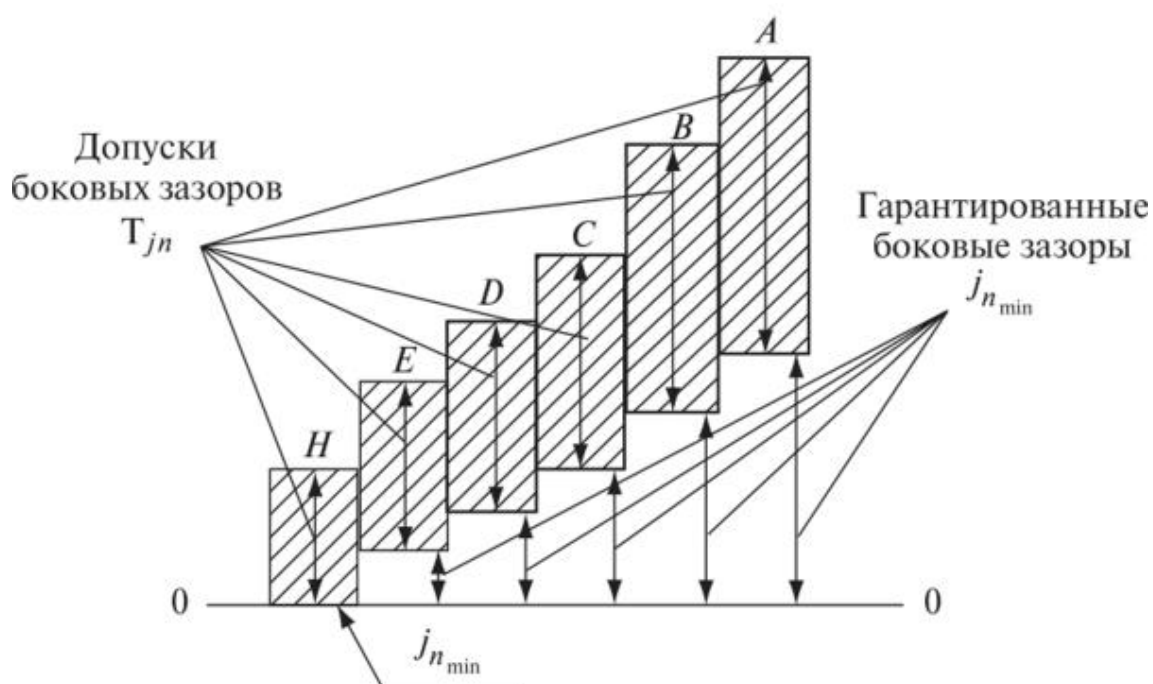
Виды сопряжения и допуски на боковой зазор.
